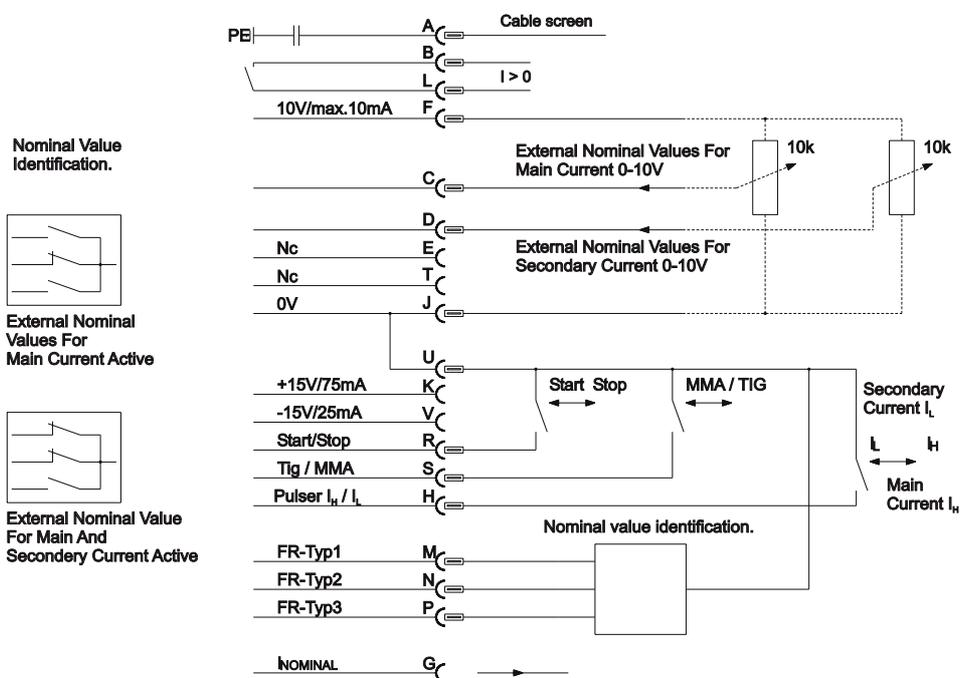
/8: Interfaz para la soldadura mecanizada, 19 polos
